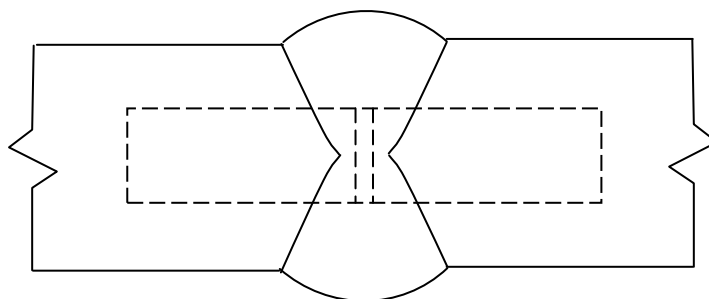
Modo de retirada dos corpos-de-prova para ensaio de impacto Charpy V em cada junta soldada.
